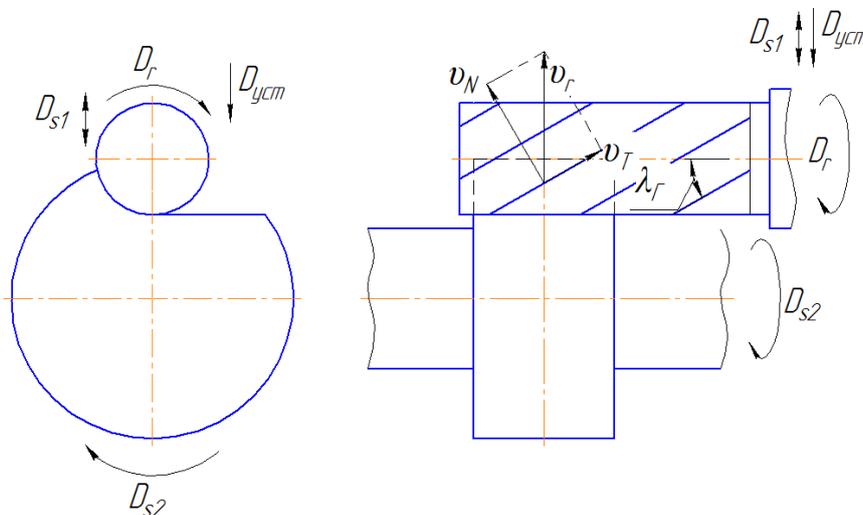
Схемы обработки плоской поверхности детали на токарно-фрезерном станке с ЧПУ
